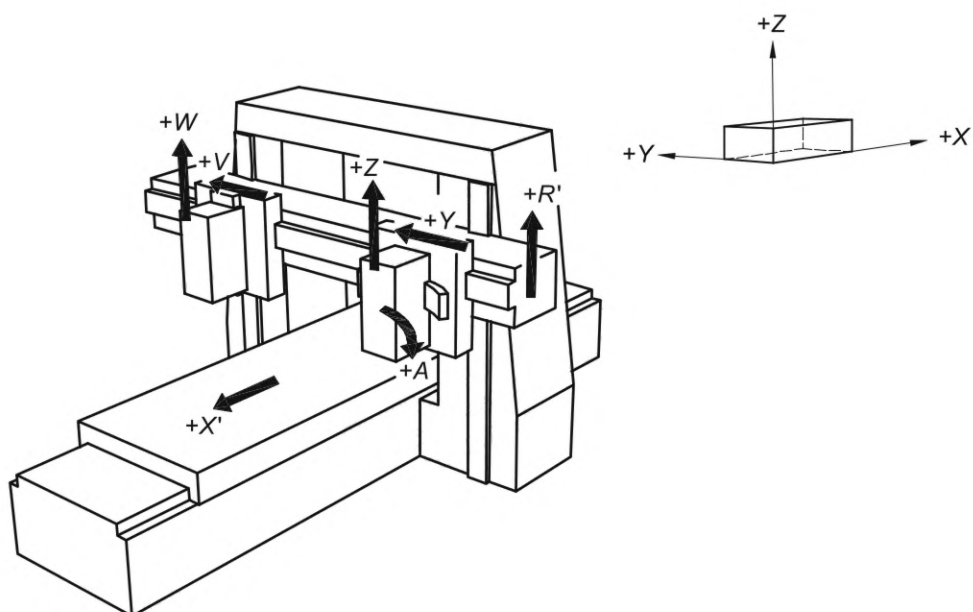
Продольно-фрезерный двухстоечный станок
